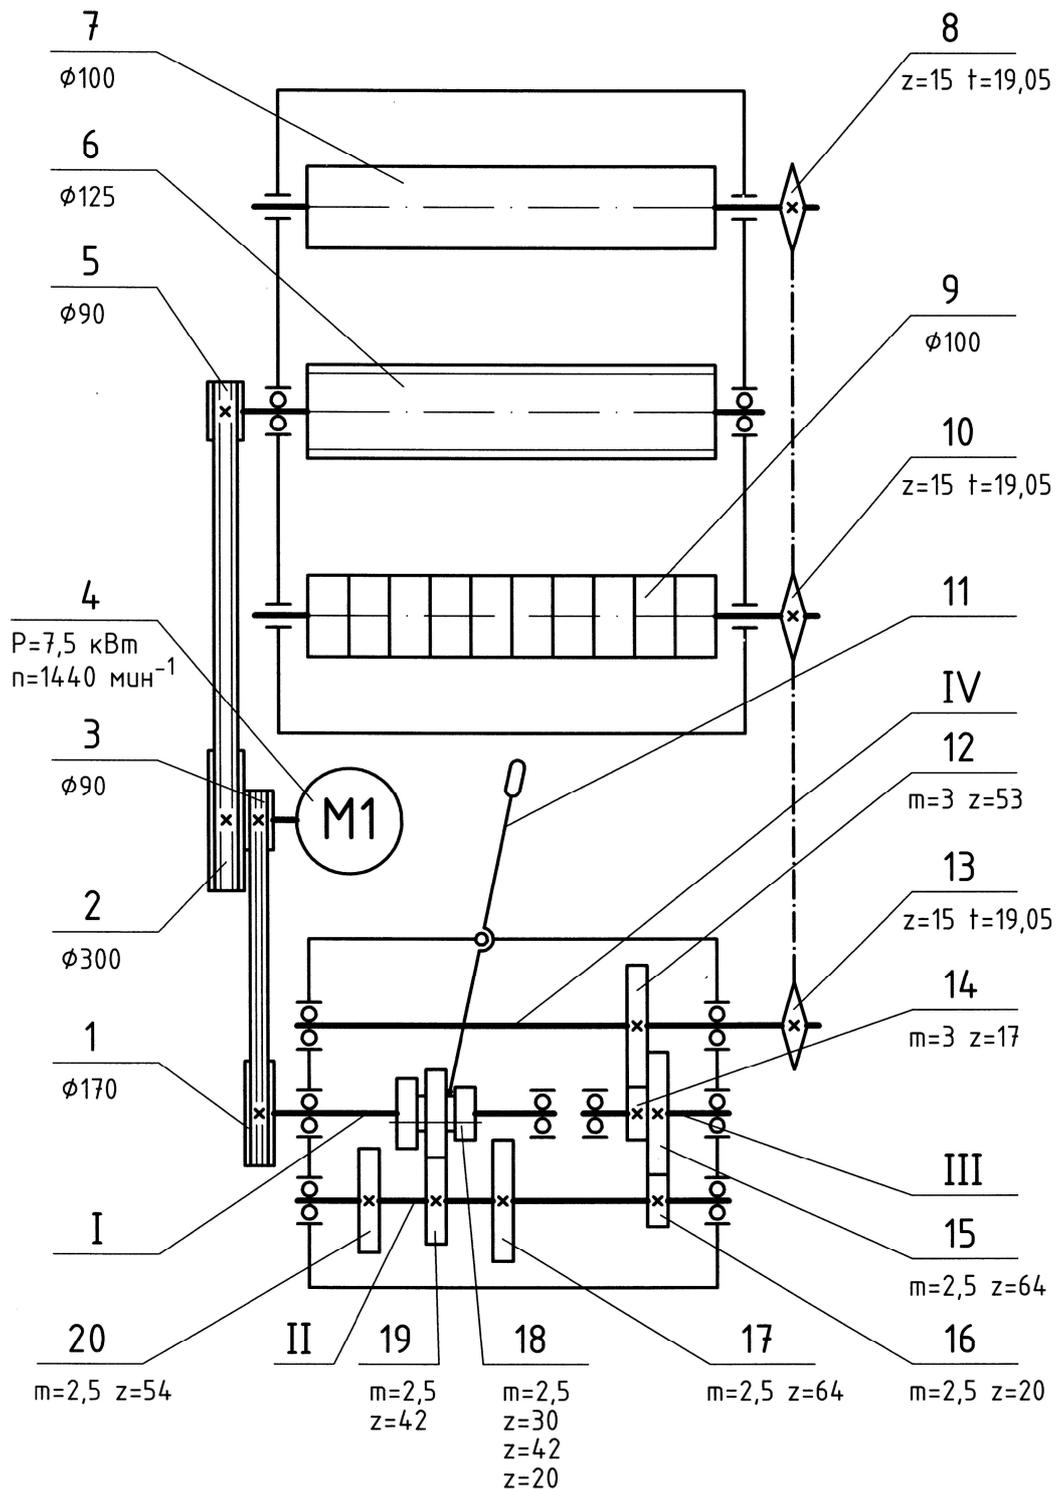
Кинематическая схема привода ножевого вала и подачи:
